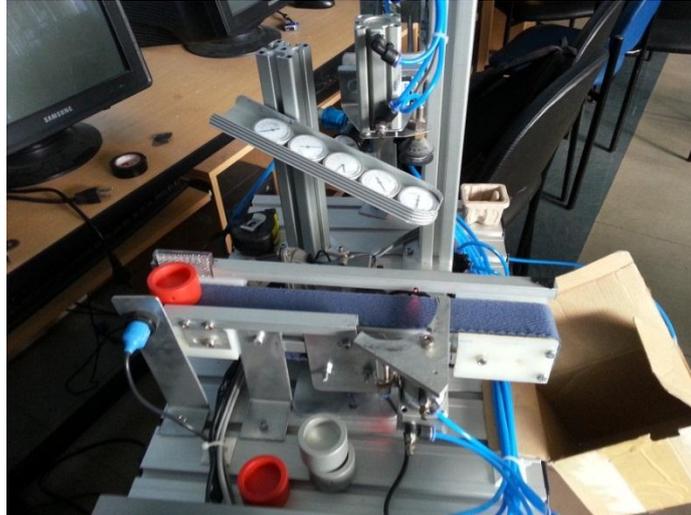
PIEZA INICIAL DE PRUEBA MECÁNICA
